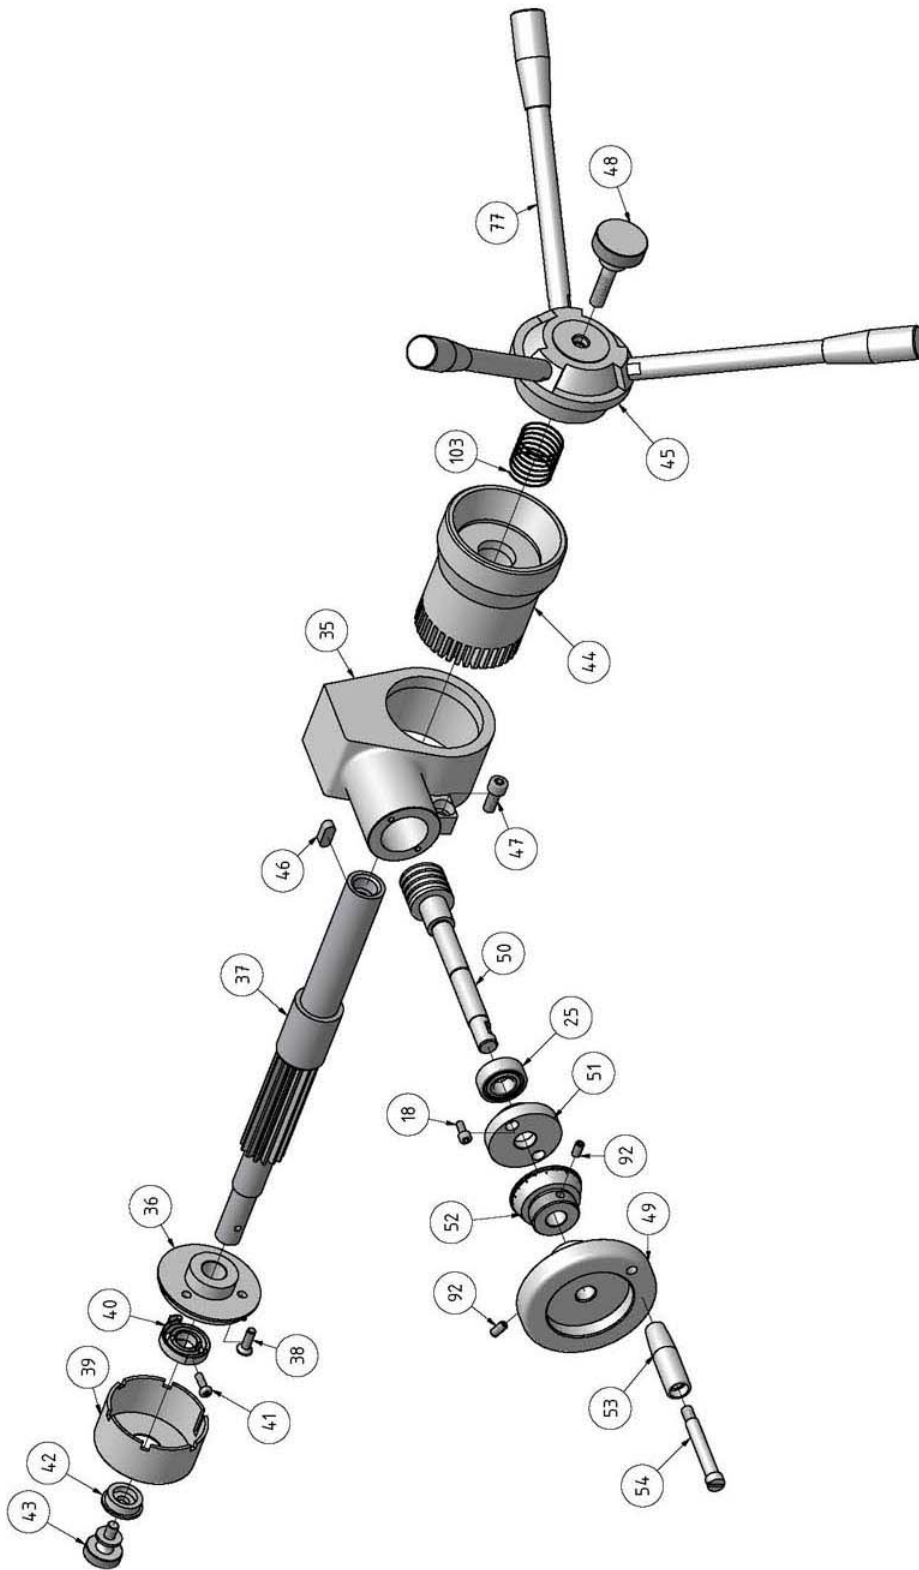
Fräskopf 5 von 6 - Milling head 5 von 6
